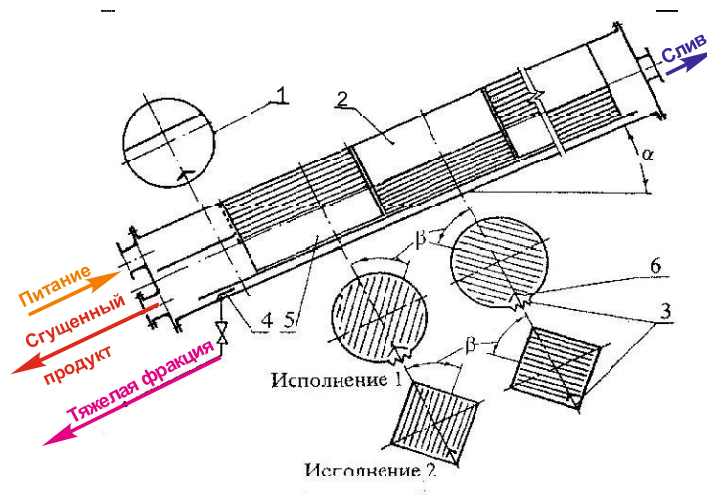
Компоновочный вариант конструкции тонкослойного аппарата: 1 – оболочка; 2 – тонкослойные секции; 3 – продольные (гофрированные) каналы; 4 – отсекающий карман; 5 – пластины; 6 – экран / Fig. 2. Layout version of the thin-layer device design: 1 – shell; 2 – thin-layer sections; 3 – longitudinal (corrugated) channels; 4 – cutting pocket; 5 – plates; 6 – screen
